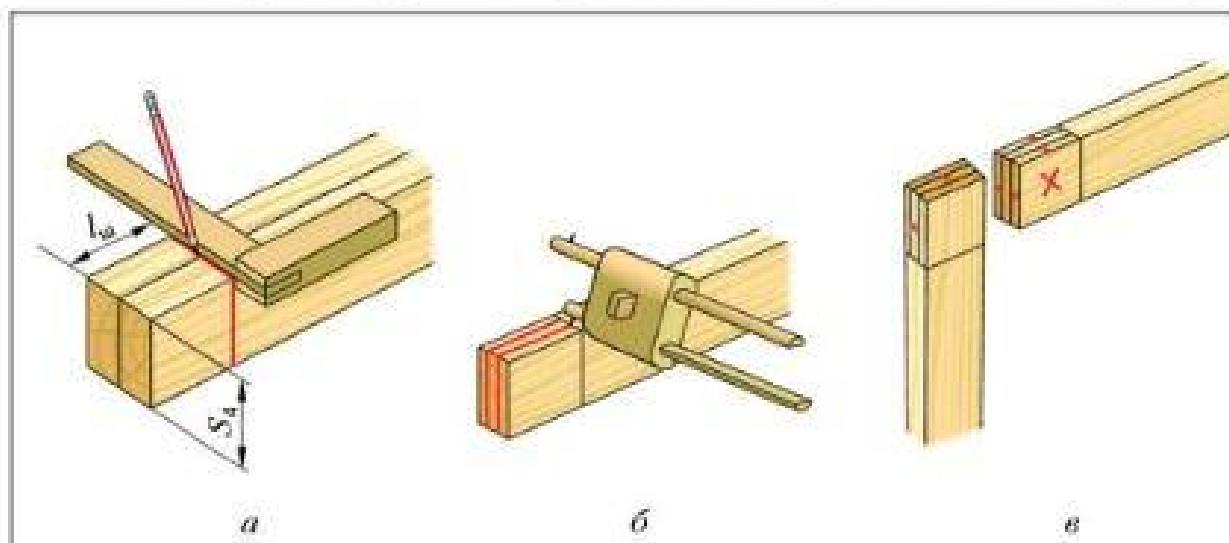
Разметка шипового соединения: *а* – разметка длины шипа; *б* – разметка толщины шипа и ширины проушины рейсмусом; *в* – маркировка вырезаемых участков
